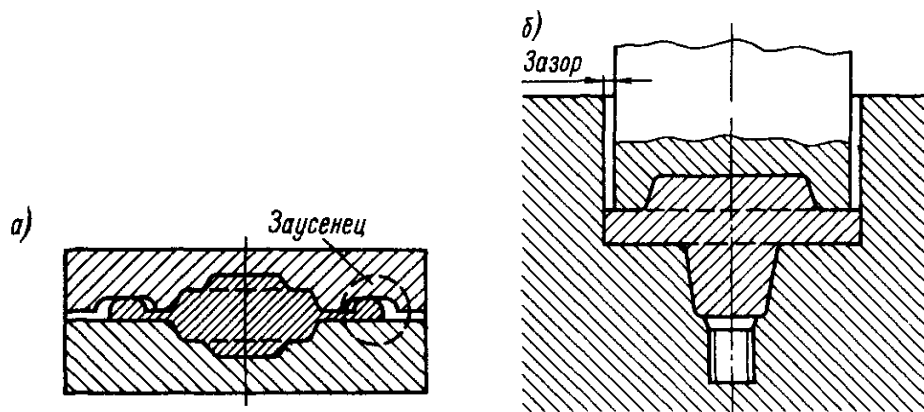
Схема открытой (а) и закрытой (б) штамповки
